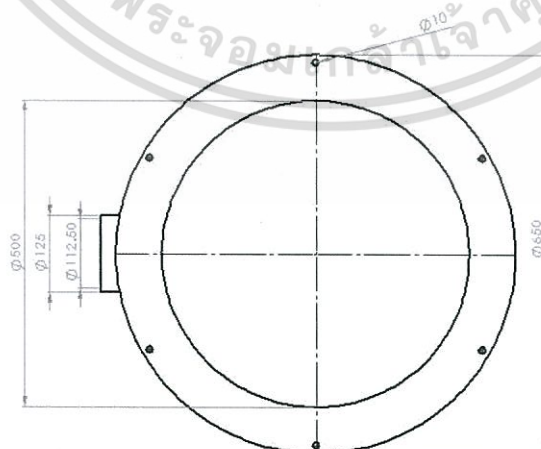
Dimension ของ Head (ด้านหน้า)
